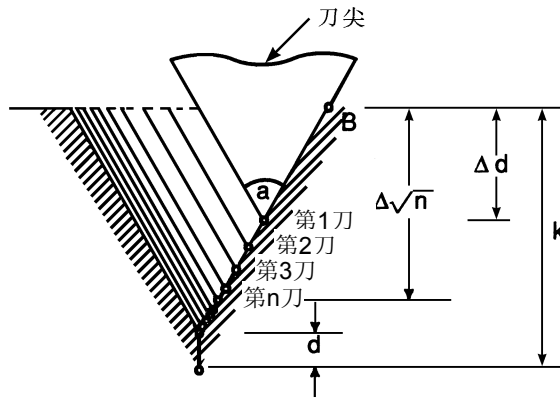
(a) 螺纹切削复循环的刀具轨迹
